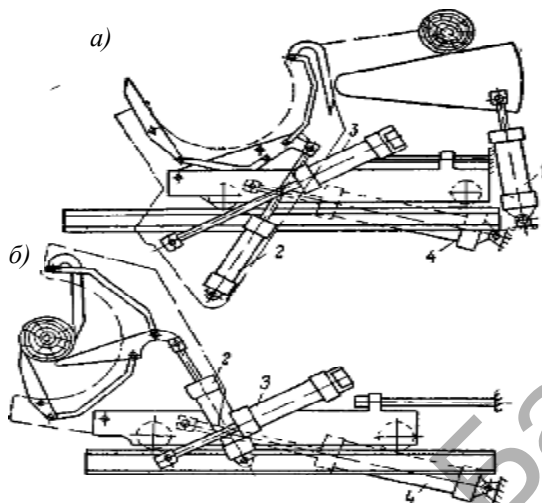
Центрирующее приспособление станка ЛУ17
